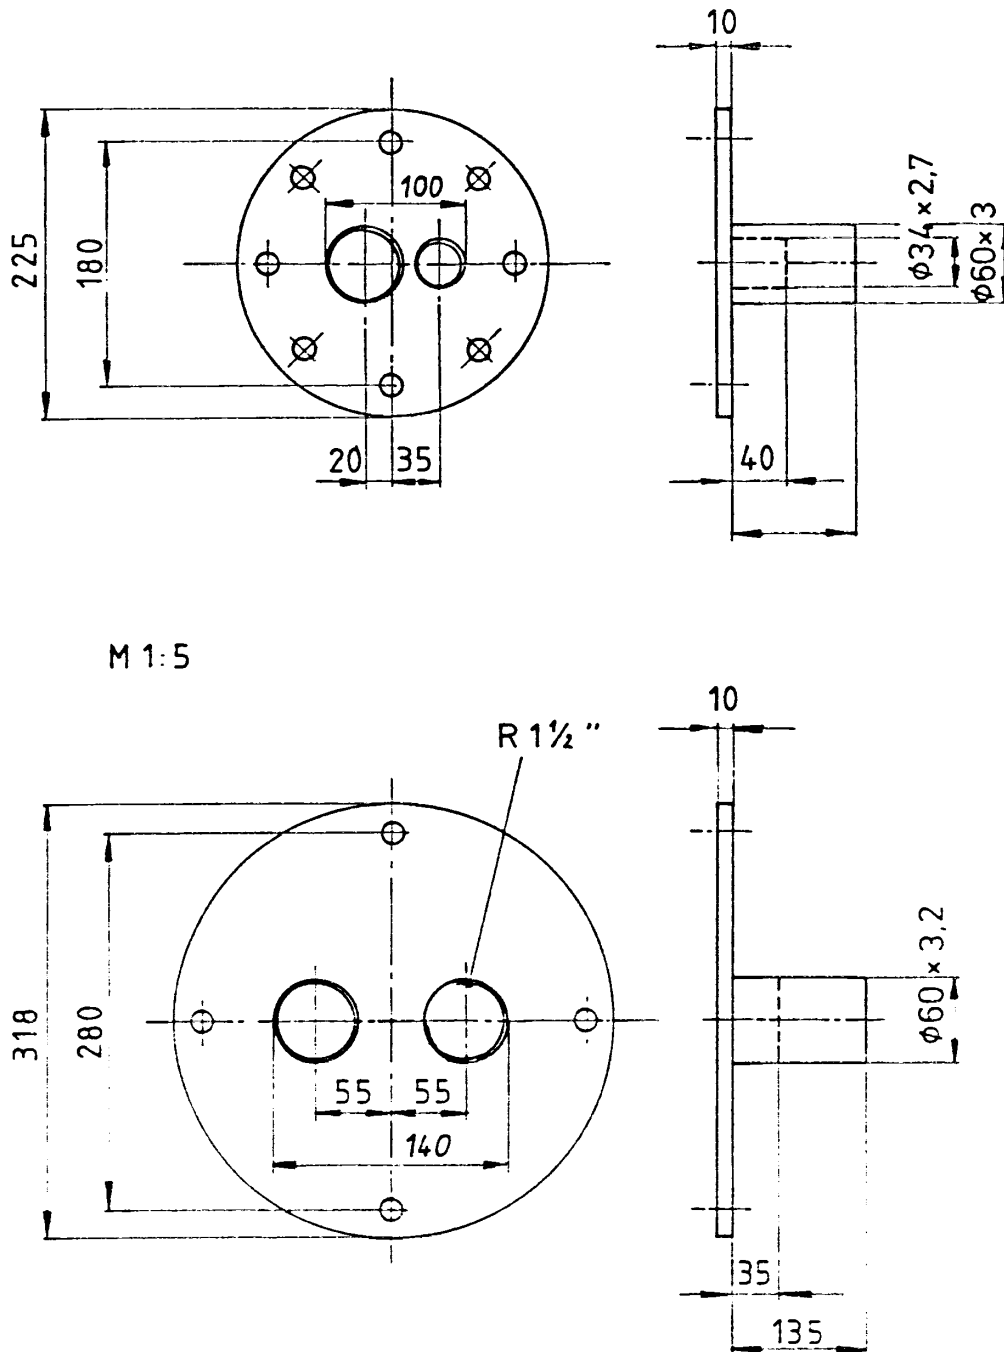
Obige Flanschplatten für den gemeinsamen Einbau von Dioxinsonde und Prandtlrohr sind vorhanden. Bevorzugt wird die Platte mit Lochkreis 280 gemäß Flansch A 200 x 219,1 nach DIN 2573 (8 Schrauben M16)
